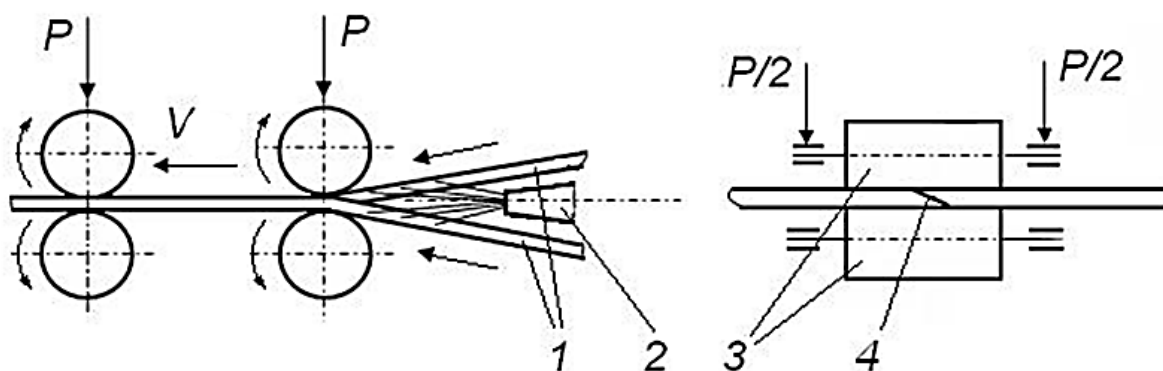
Схема зварювання нагрітим газом без присадного матеріалу: 1 - зварювальні листи; 2- сопло пальника; 3-притискні ролики; 4-зварний шов.
